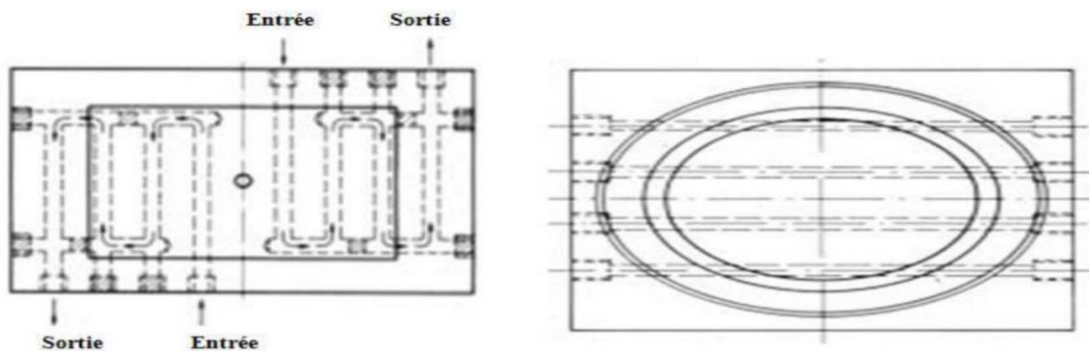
Circuit de refroidissement des plaques de moule [29]
